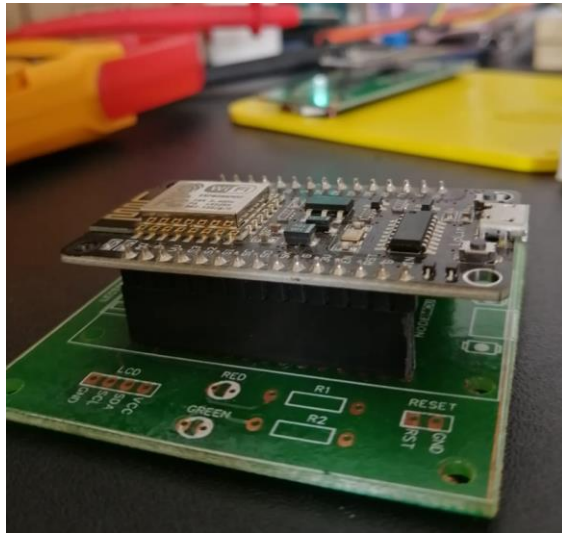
Soldadura de Conectores Heder para Montaje del Microcontrolador.
